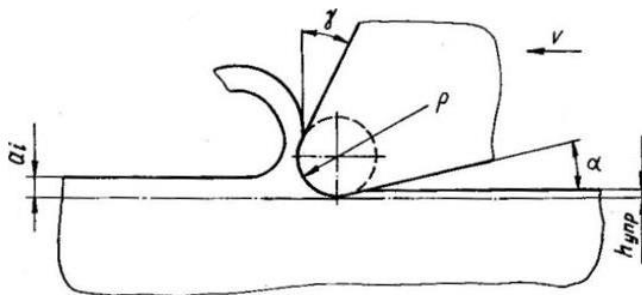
Схема врзання зуба фрези при зубофрезеруванні зубчастих коліс
